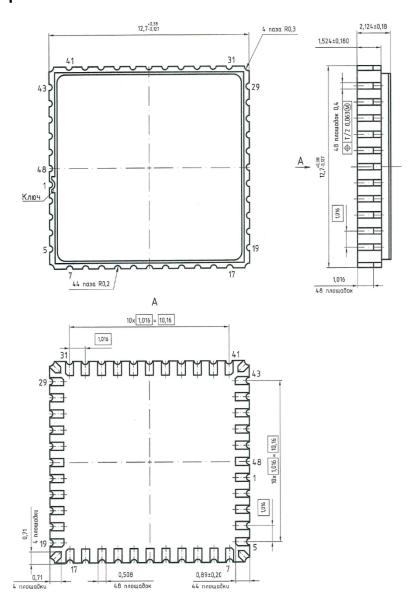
Габаритный чертеж корпуса 5142.48-А (размеры в мм)
